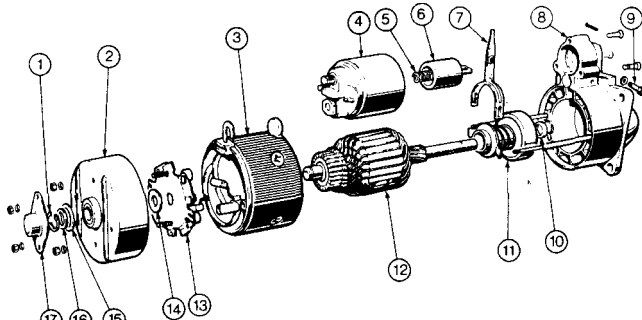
Разобранный стартер CAJAVEC. 1 - Е-образный стопор. 2 - Задняя крышка. 3 - Основной корпус. 4 - Корпус реле. 5 - Пружина. 6 - Якорь. 7 - Пусковой рычаг. 8 - Крышка со стороны привода. 9 - Поворотная шпилька. 10 - Пружинное кольцо. 11 - Агрегат ведущей шестерни и муфты свободного хода. 12 - Якорь. 13 - Пластина щеток. 14 - Тормозное кольцо. 15 - Уплотнительное кольцо. 16 - Расширяющая прокладка. 17 - Колпачок.
